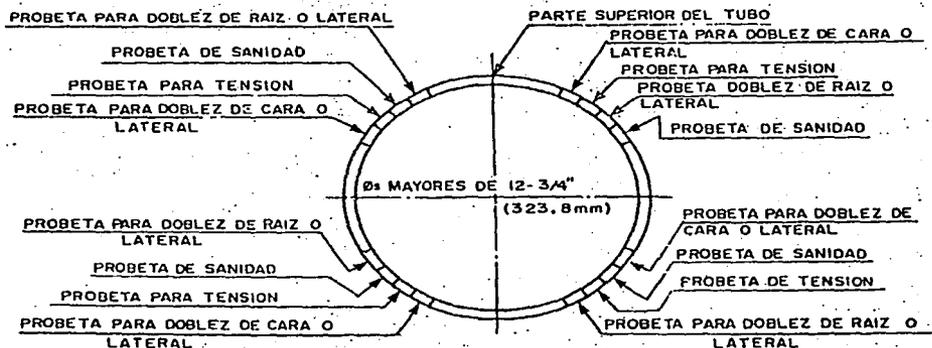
Localización de las Probetas Para Ensayos en las Soldaduras
